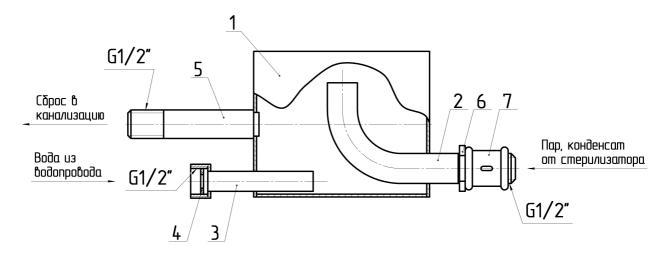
Схема и устройство парогасителя ЦТ129М.70.000 1- Корпус; 2- Патрубок ввода пара; 3- Патрубок ввода воды; 4- Шайба; 5- Патрубок выпуска пара; 6- Гайка; 7- Муфта
